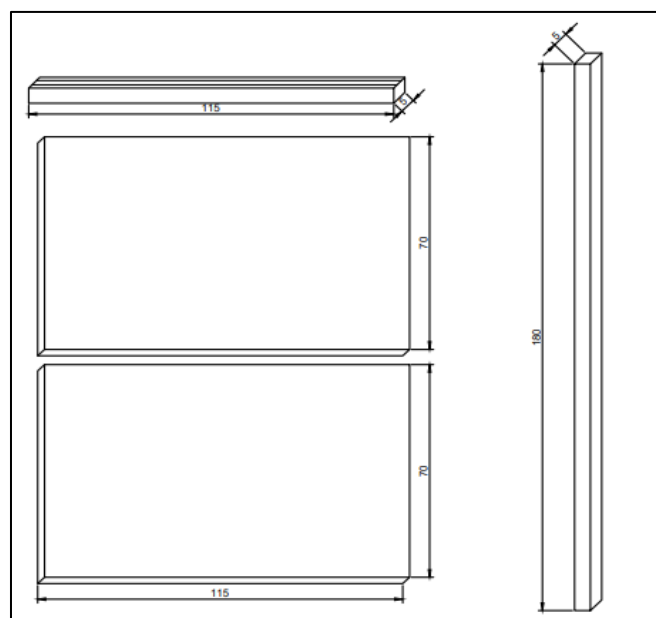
Material utilizado para la construcción estructural del módulo.
